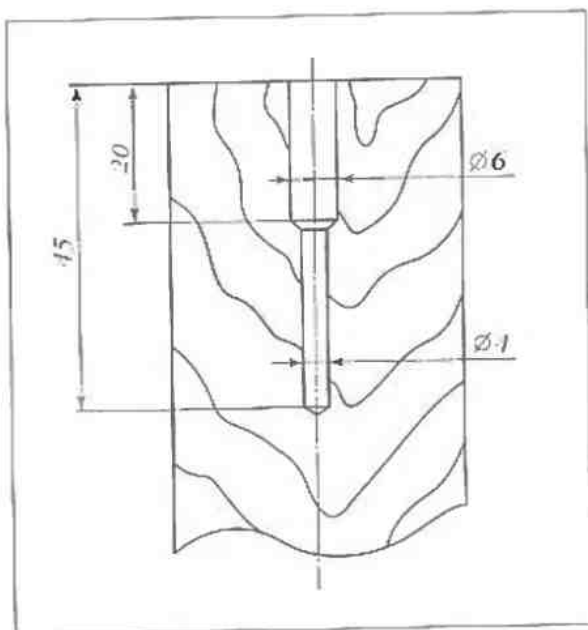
Схема сверления отверстия в заготовке рукоятки под остроугольный хвостовик
